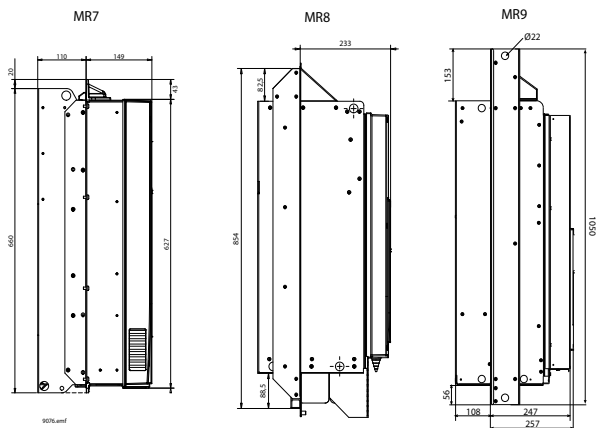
MR7 ao MR9, montagem com flange, dimensões de profundidade
